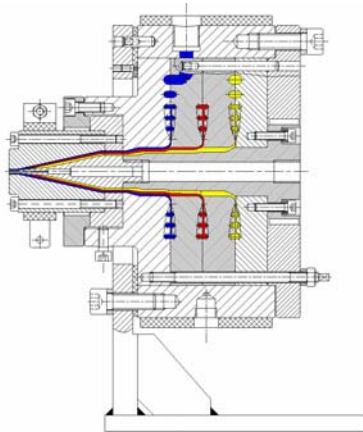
3-Schicht Werkzeug für Medizinschläuche
